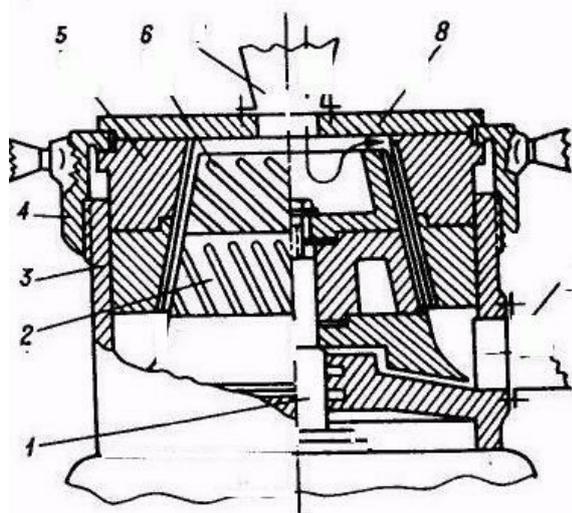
Конусная коллоидная мельница: 1 – вал; 2 – ротор; 3 – корпус; 4 – накидная гайка; 5 – статор; 6 – канавки; 7 – приемная воронка; 8 – крышка; 9 – выводной штуцер
